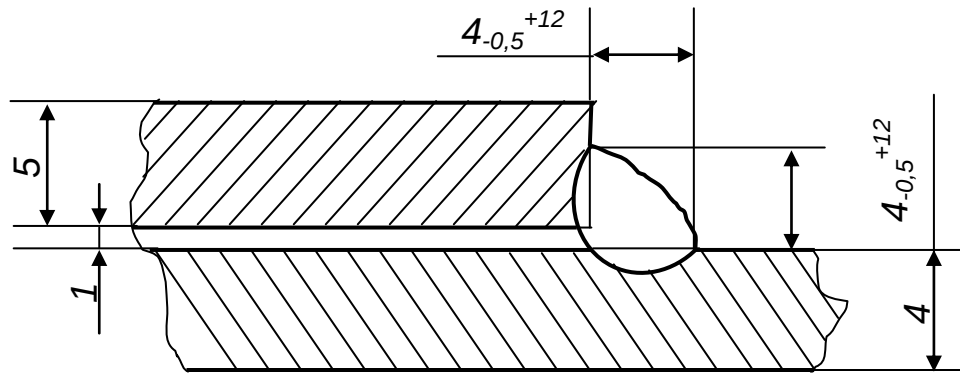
Схема зварного з'єднання механізованого зварювання в суміші захисних газів плавким електродом
